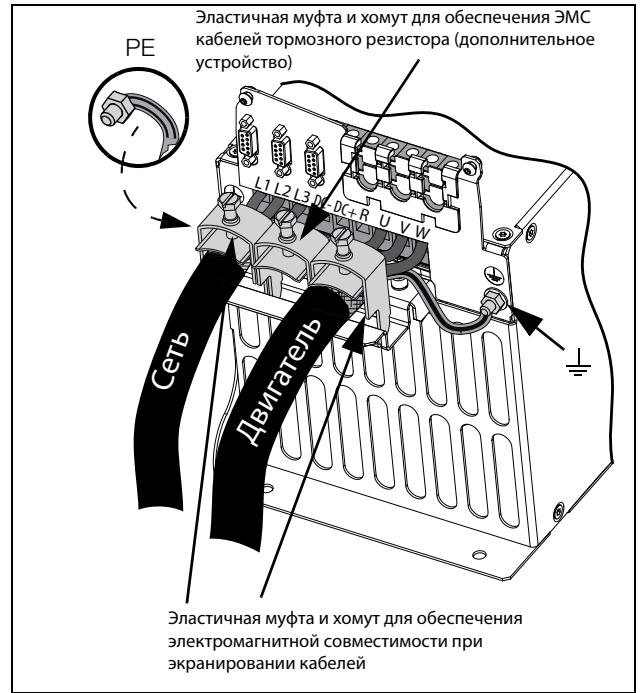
Подключение сетевого питания и двигателя моделей 48-025 — 48-058, размер корпуса С2 и моделей 69-002 — 69-025, размер корпуса С2(69)
